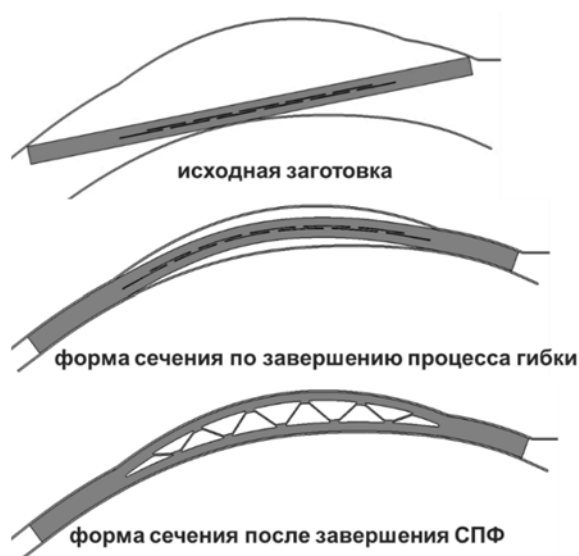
Этапы процесса гибки и формовки сечения лопатки
